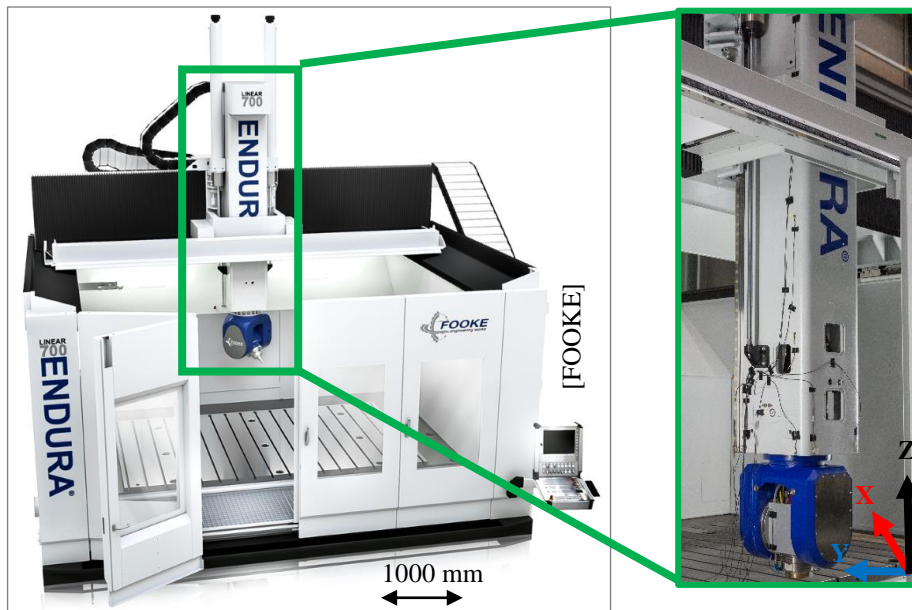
Beispielhafte Werkzeugmaschine mit dem konventionellen Z-Schlitten
